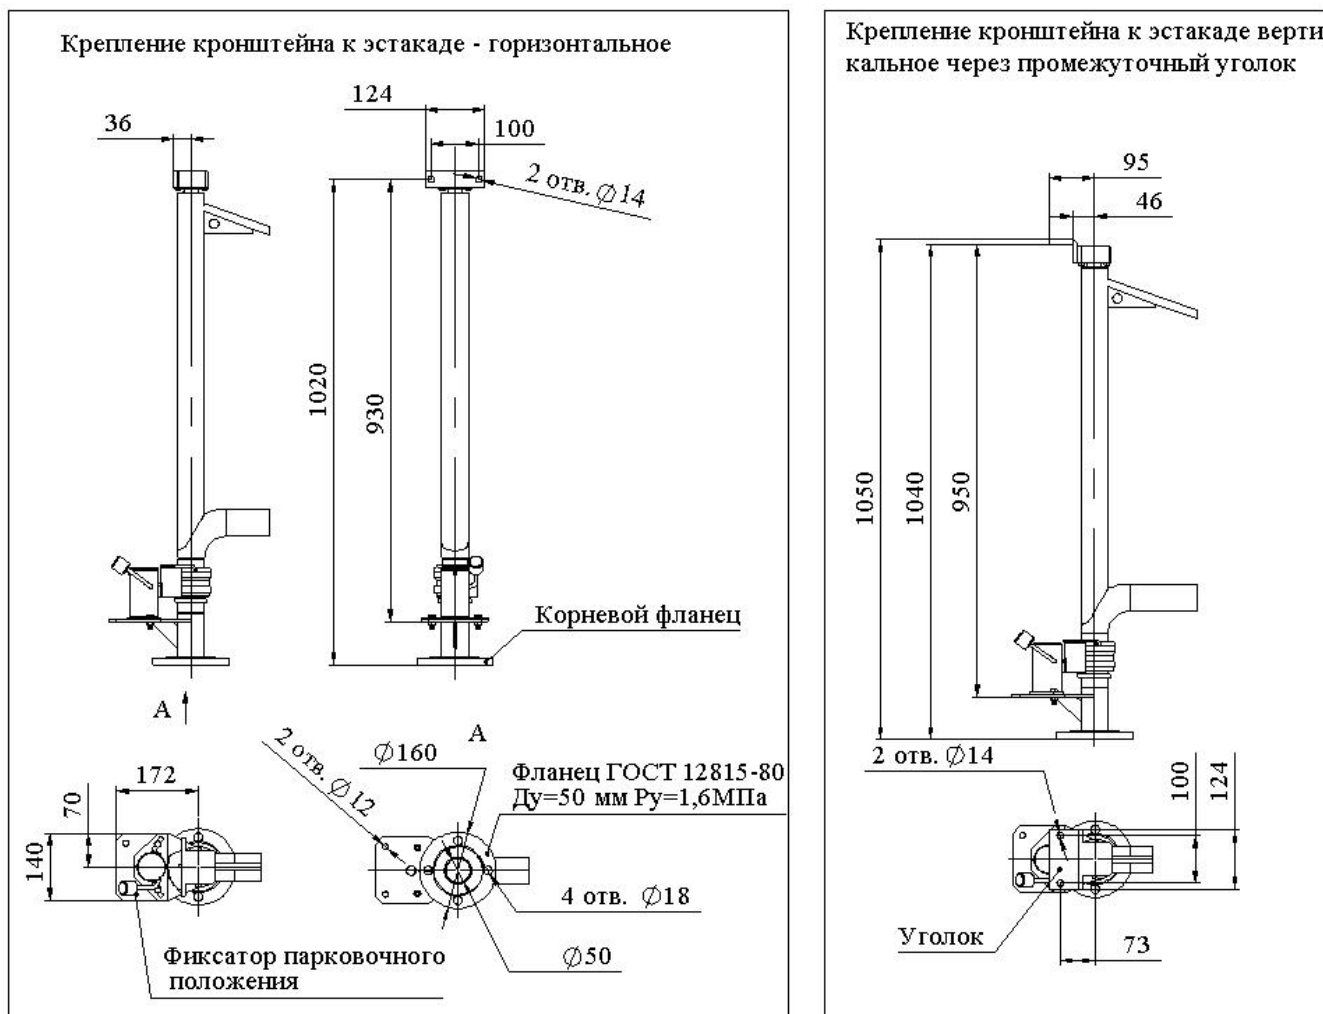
Установочные размеры стояка слива-налива жидкой фазы.
